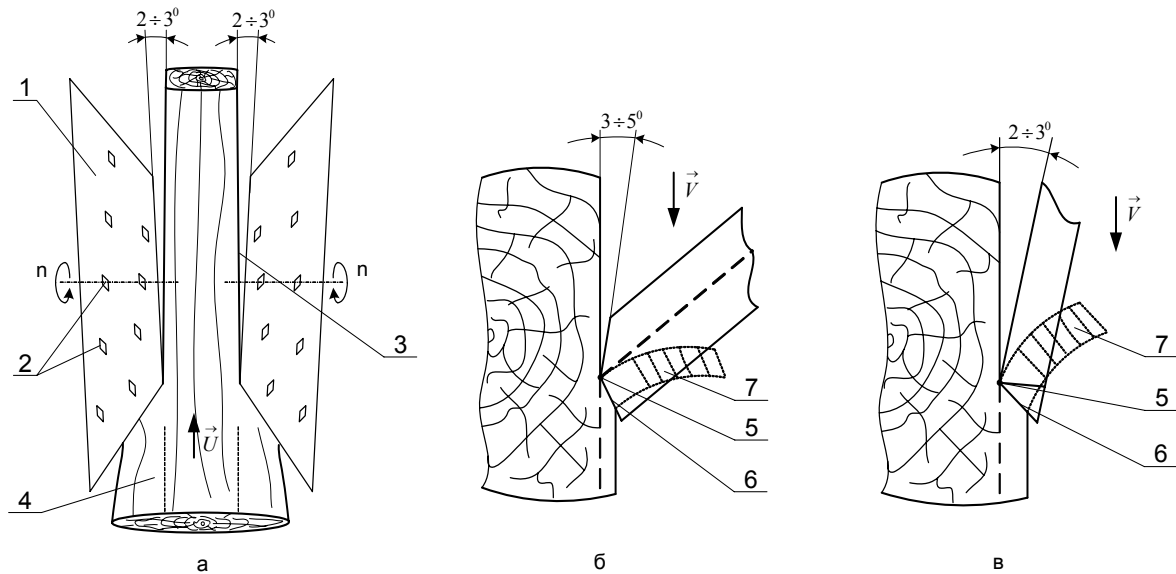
Схема резания на фрезерно-брусующих станках двухлезвийными резцами:
